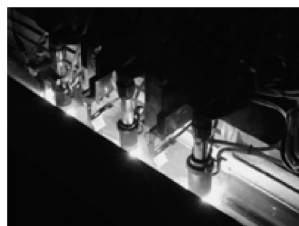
SPBタンクの外板を3電極自動溶接装置でMIG溶接
